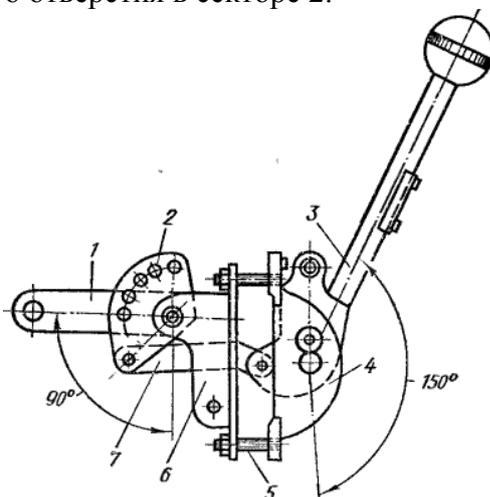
Рычажный привод ПР-2: 1 — рычаг, 2 — сектор, 3 — рукоятка, 4 и 6 —
